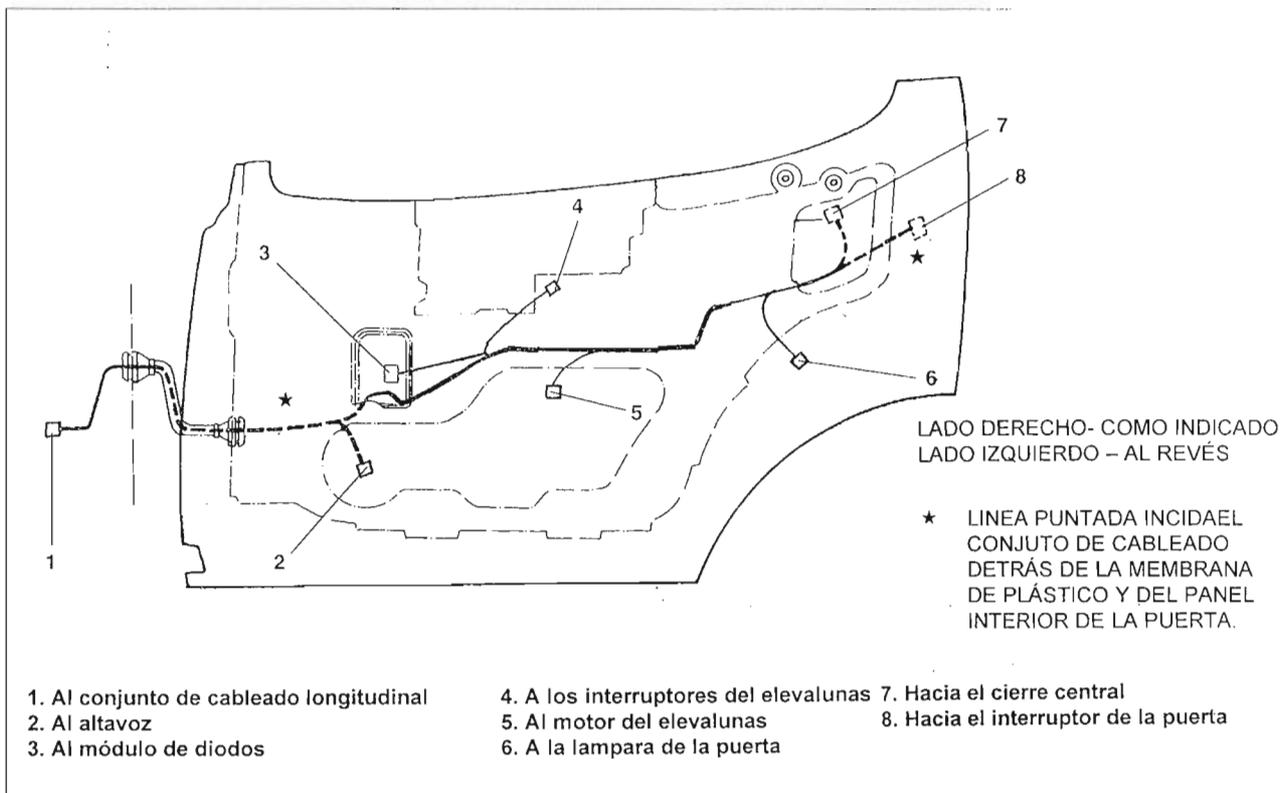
Conjuntos de cableado de la puerta trasera izquierda /derecha
